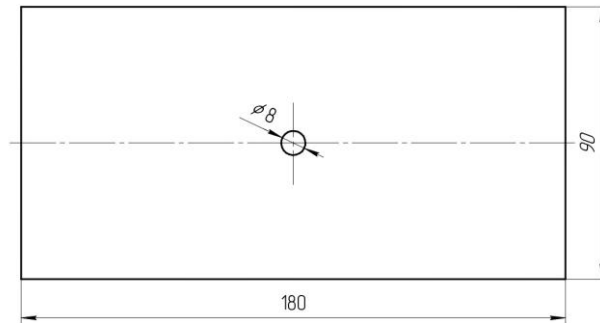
Фронтальное изображение корпуса приспособления для полировки
